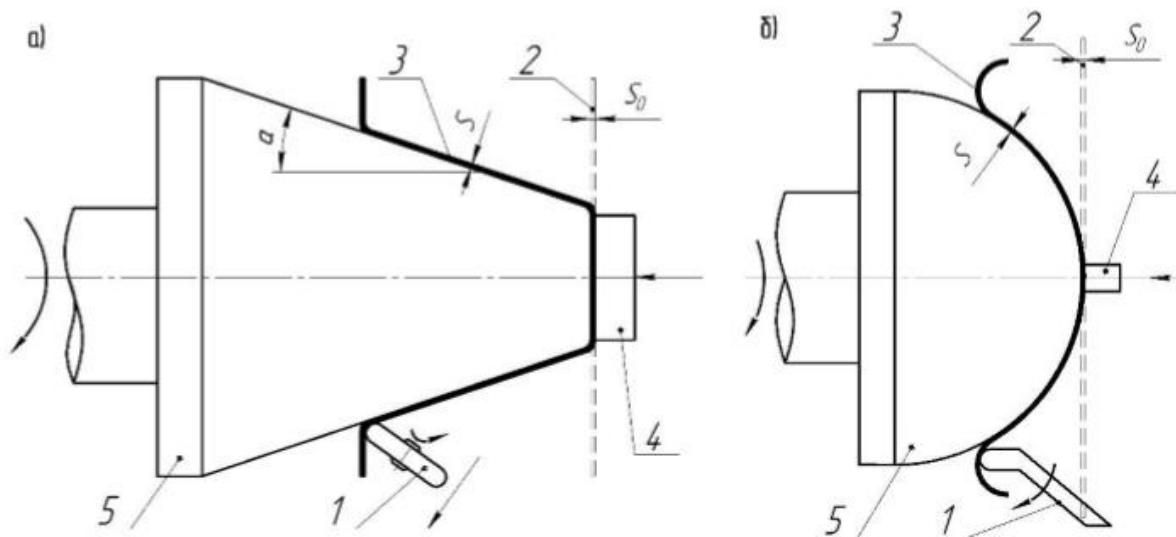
Схеми одержання заготовок методами точкового деформування: а – ротаційне витягування конусоподібної деталі; б – ротаційне витягування сферичної деталі; 1 – формоутворювальний інструмент; 2 – листовая заготівля; 3 – деталь, що виготовляється; 4 – притиск; 5 – оправлення
